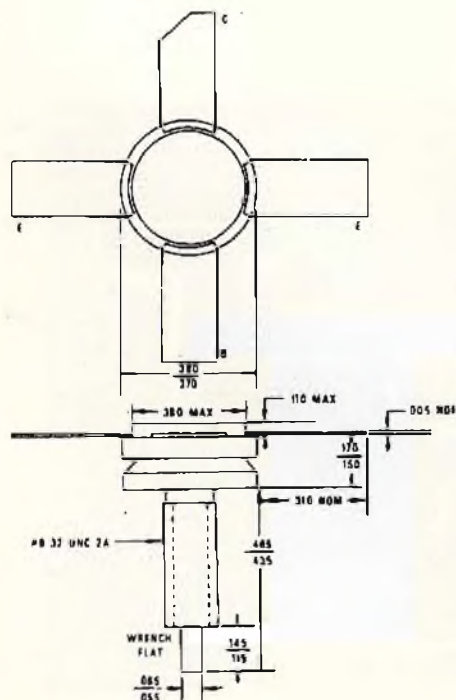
Vista in pianta e profilo di uno «stripline» tipico.
